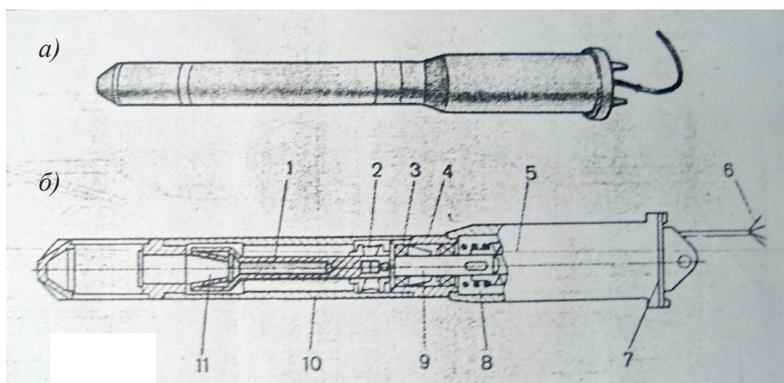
Навесной глубинный электрический вибратор ИВ-114: а – внешний вид; б – разрез; 1 – бегунок-дебаланс; 2 – упругая муфта; 3 – подшипник; 4 – корпус шпинделя; 5 – электродвигатель; 6 – кабель; 7 – крышка; 8 – кулачковая муфта; 9 – шпиндель; 10 – корпус вибронаконечника; 11 – сердечник
